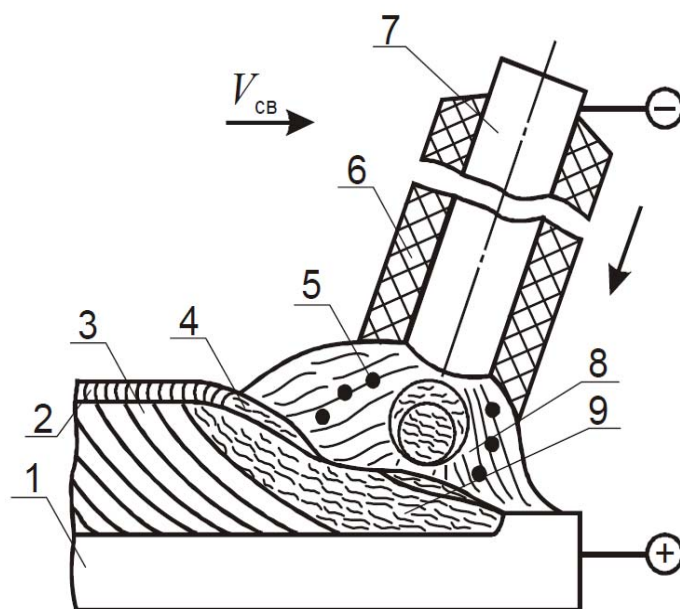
Схема процесса сварки металлическим электродом с покрытием
